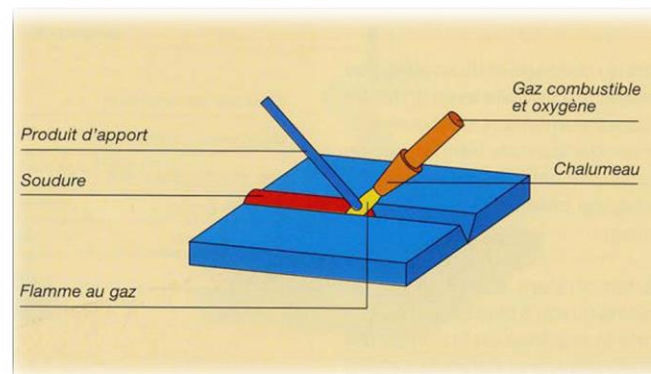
Principe du soudage oxygaz [22].
